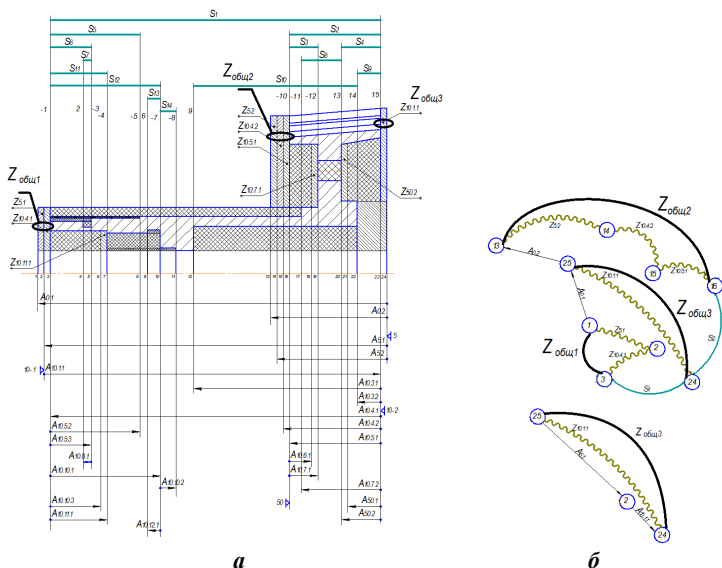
Схема припусков (а) и графы размерных цепей заготовки (б)
